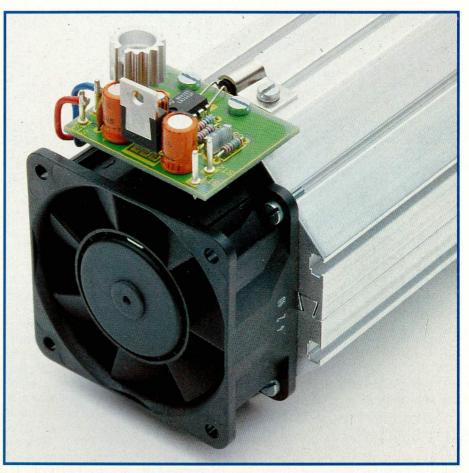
Angeschraubte Lüftersteuerung, zusammen mit ELV-Profil LK 75 und Lüfter Typ 612. Der Sensor wird mit einer Schelle auf den Kühlkörper gepreßt.
